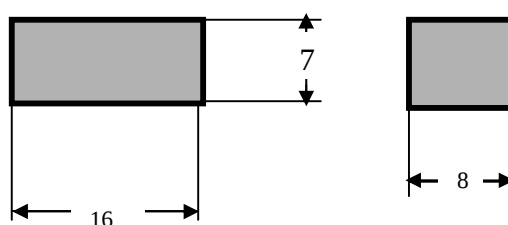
Probeta rectangular para ensayo de Dureza (medidas en mm)
